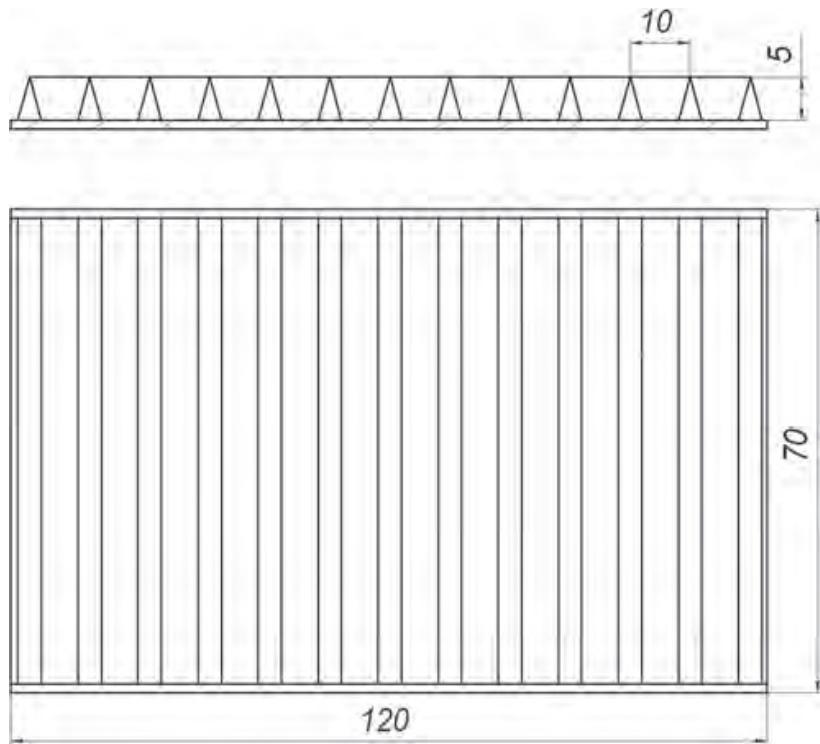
Приспособление для изготовления пластиноч из краски [4]
